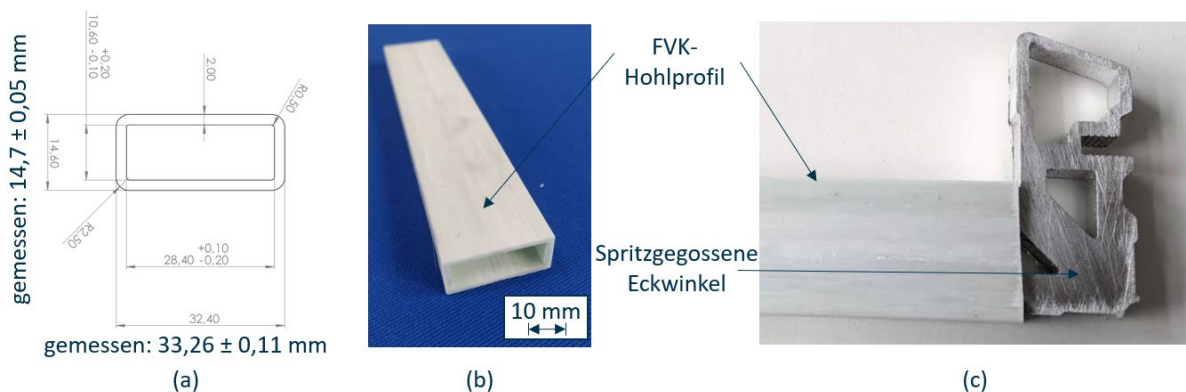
Zeichnung und gemessene Dimensionen des Hohlprofils (a). Gefertigte FVK-Hohlprofile (b) und Montage mittels spritzgegossener Eckwinkel (c).
